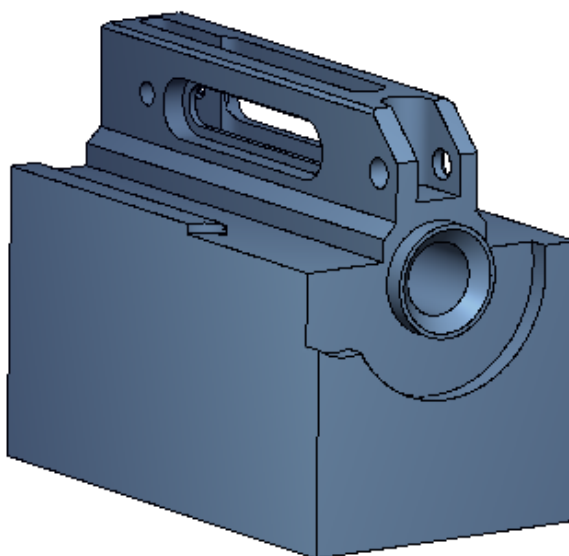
Obrobek po frézování na hrubo a dokončovacím frézování.
